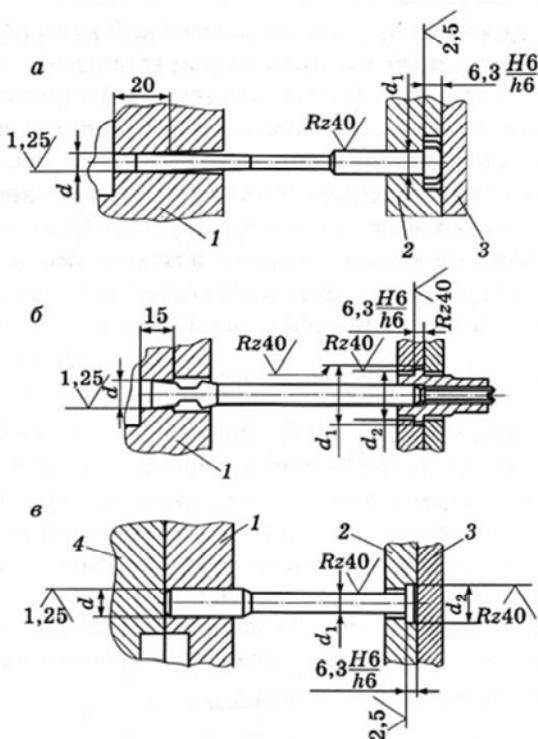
Примеры установки выталкивателей и контролокателей:
